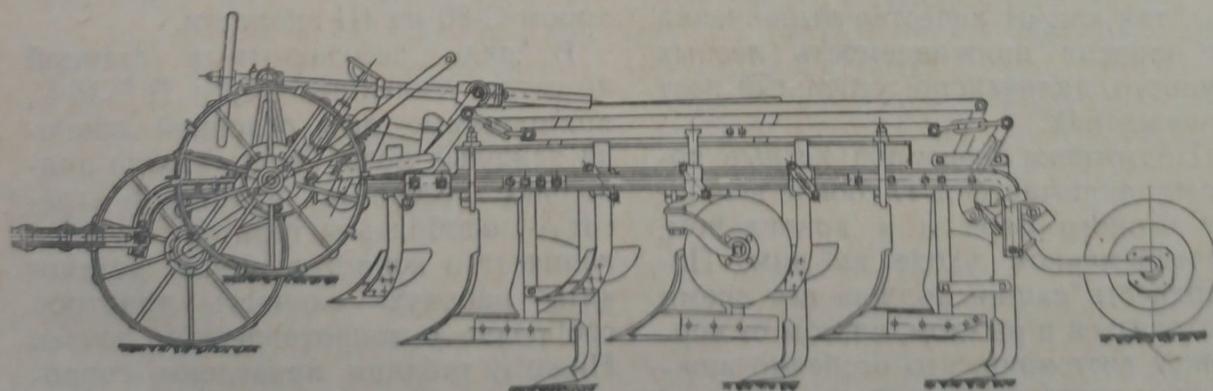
Трехкорпусный плуг с почвоуглубителями ПЗ-30-П.
